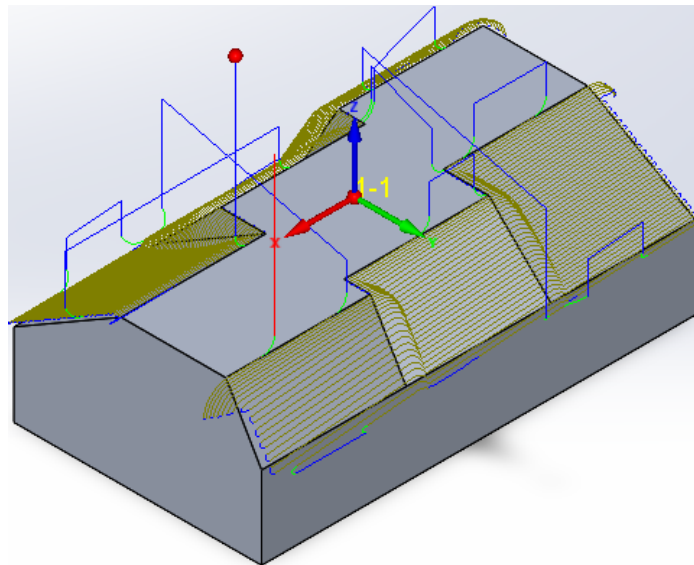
Trajetória executada durante a operação de maquinagem linear turbo
